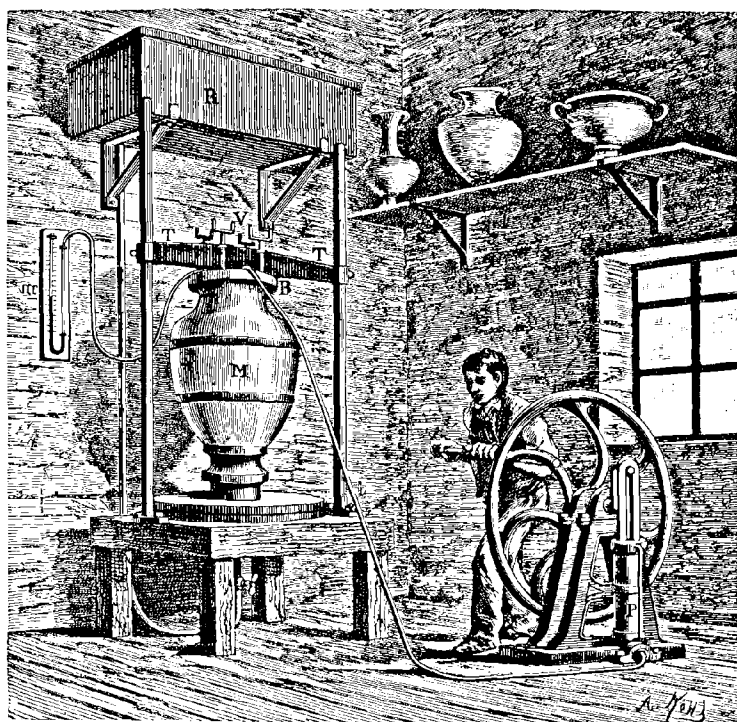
Appareil à air comprimé pour le coulage des grandes pièces.
